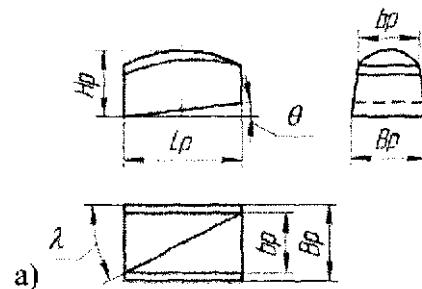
Конструкции резцов-зубьев развёртки с регулированием безвершинных зубьев
